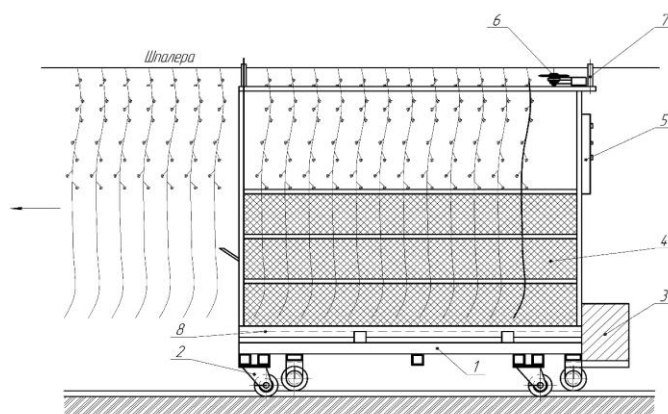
Предлагаемая машина для уборки растительных остатков: 1 – рама; 2 – колёса опорные; 3 – привод; 4 – бункер; 5 – пульт управления; 6 – режущий элемент; 7 – ролики направляющие; 8 – платформа подъёмная.
